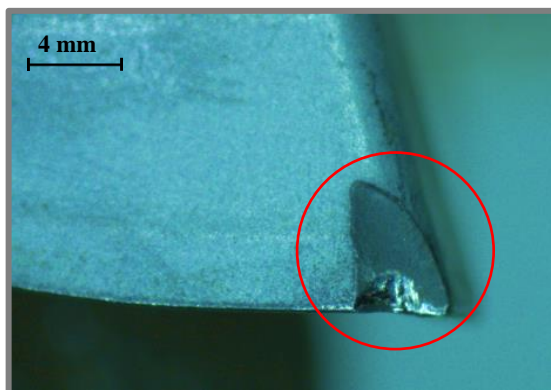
Estado do inserto após usinagem do passe 16\*.
